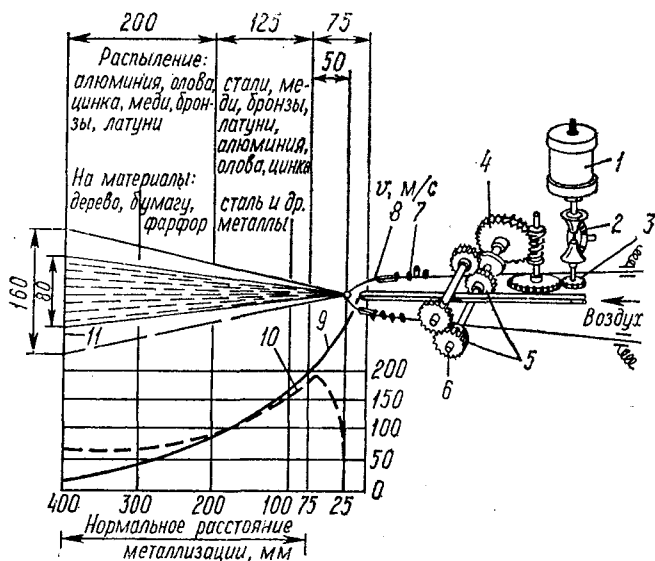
Кинематическая схема электродугового металлизатора и процесс распыления металла:
